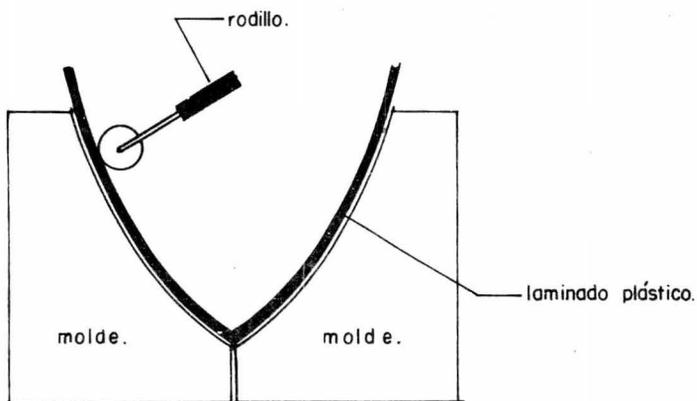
REFORZADO.- MOLDEO POR CONTACTO.
